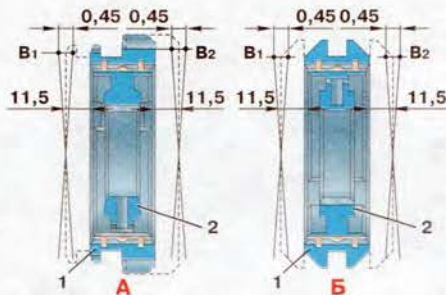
Комплектование и подбор деталей синхронизаторов коробки передач: А – синхронизатор I и II передач; Б – синхронизатор III и IV передач; 1 – муфта; 2 – ступица
